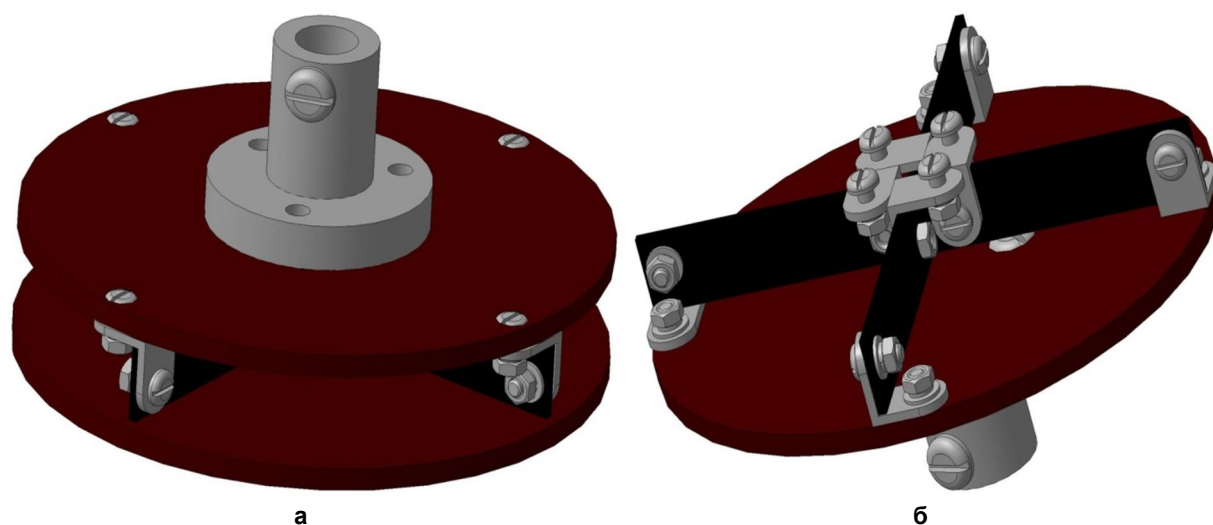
Корпус датчика: а – фланец и диски; б – упругие пластины
